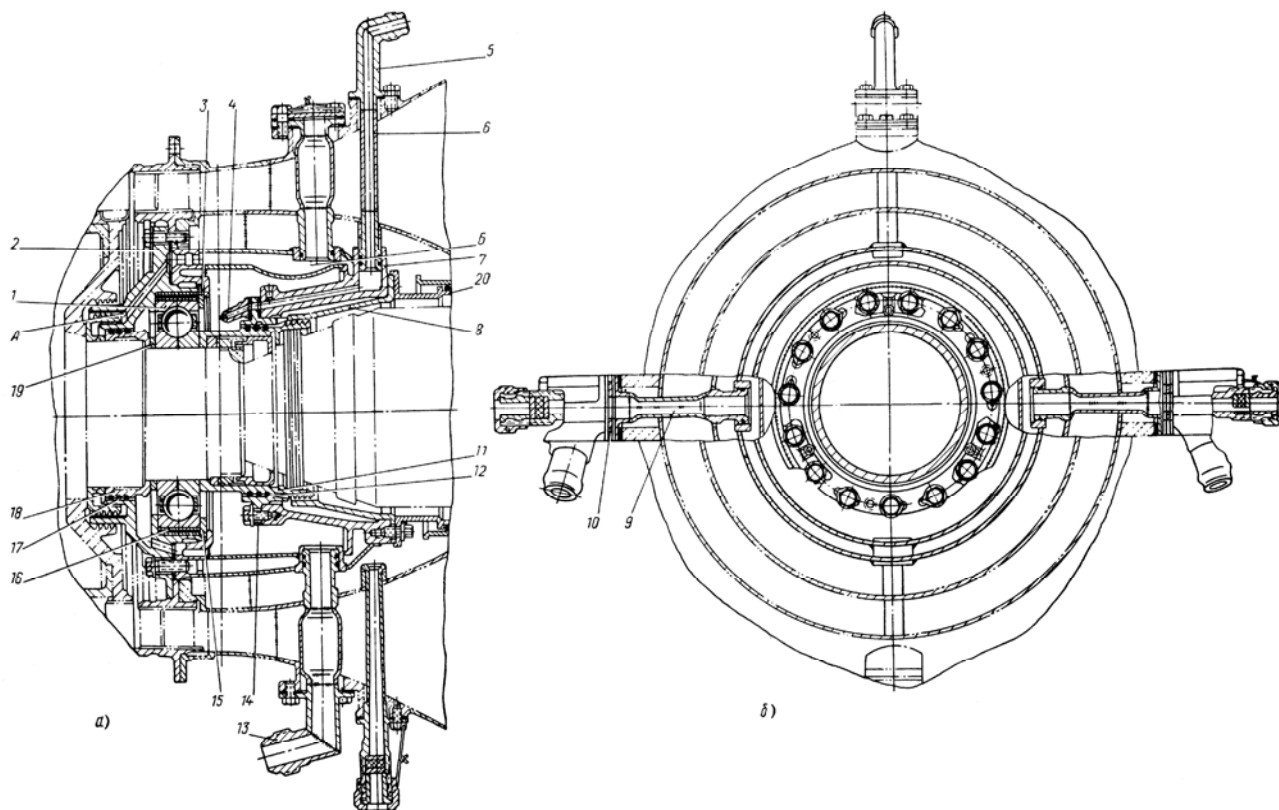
Вторая опора роторов двигателя (разрез и вид спереди):
